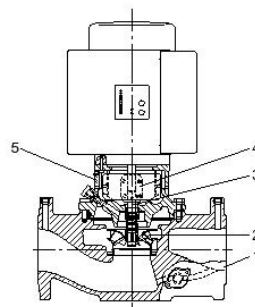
Rysunek przekrojowy pompy TP Seria 100 (z przyłączem gwintowanym)
